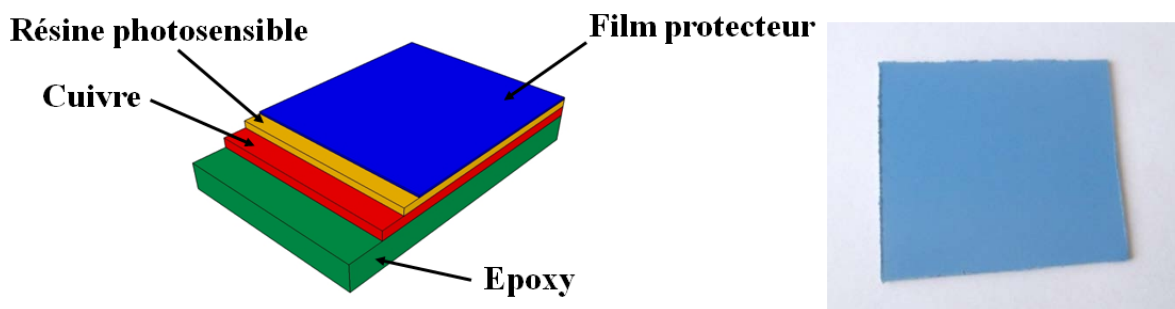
(a) Structure 3D de la plaque PCB (b) photographie de la plaque PCB
